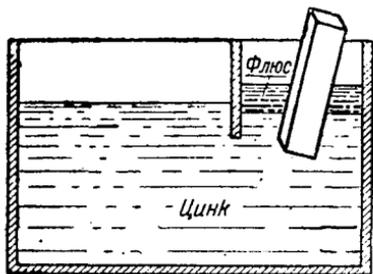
Погружение детали в расплавленный цинк через слой флюса
